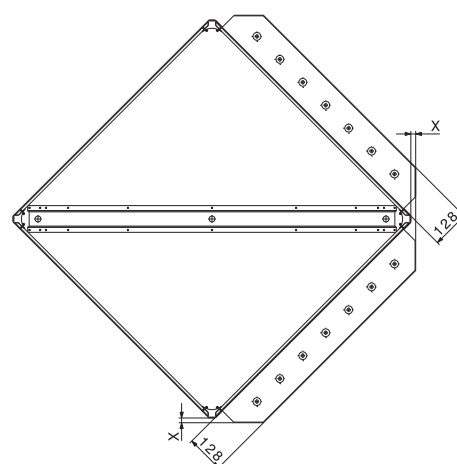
Maßblatt für Plattenwärmetauscher der Ausführung F mit Klappen (Maße in mm)
